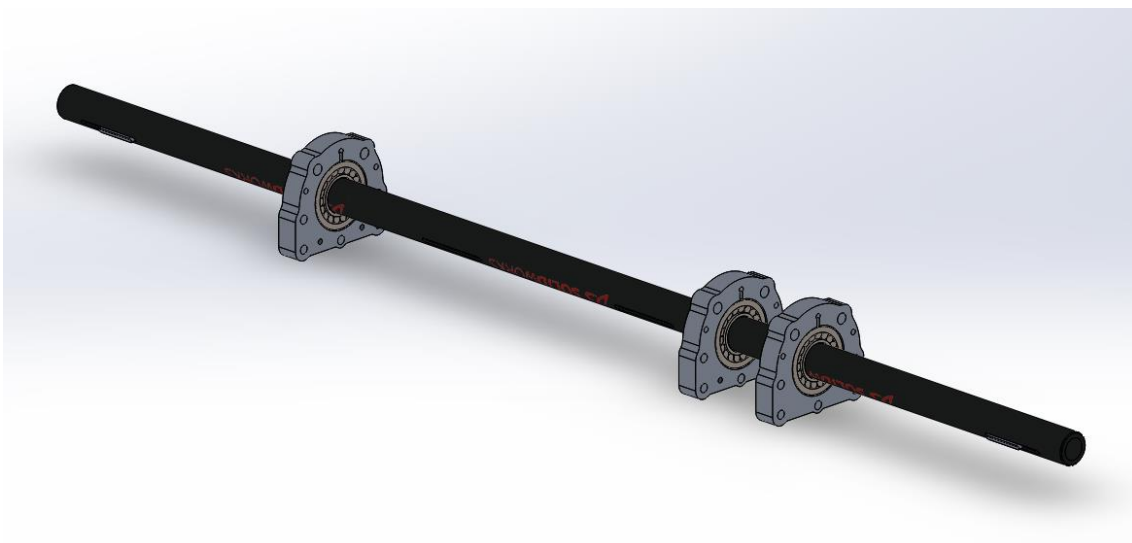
conjunto eje-rodamiento-porta rodamiento. Fuente: propia.
